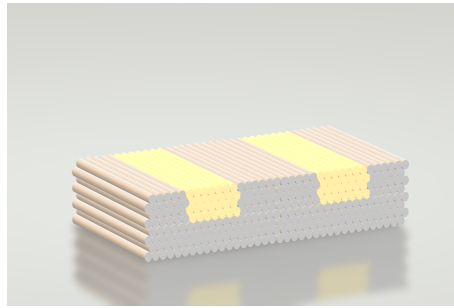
Kontaktování nevodivým lepidlem - Finální stav
